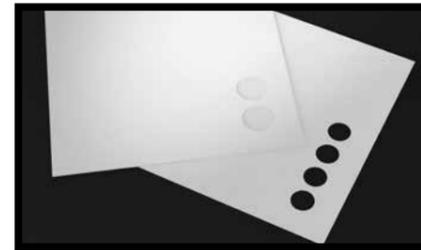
Alle KERLITE-Typen können auch mit CNC-Maschinen gebohrt werden. Zuerst eine Vorbohrung mit einer Diamantbohrspitze fertigen, dann notfalls die Bohrung mit einem Fräser auf die gewünschte Größe erweitern. Eine Bohrspitze im Durchmesser zwischen 4 und 8 mm verwenden. Die Arbeitsgeschwindigkeit beträgt 40 mm/min. mit 900 Upm Spindelrotation. Mit diesen Werkzeugen wird folgendes empfohlen: Die An-schneidstelle mit Wasser abkühlen, mit niedriger Drehgeschwindigkeit zu bohren beginnen, einen nicht zu starken Druck ausüben und diesen auf jeden Fall je nach der Festigkeit des bearbeiteten KERLITE Typs anpassen.
